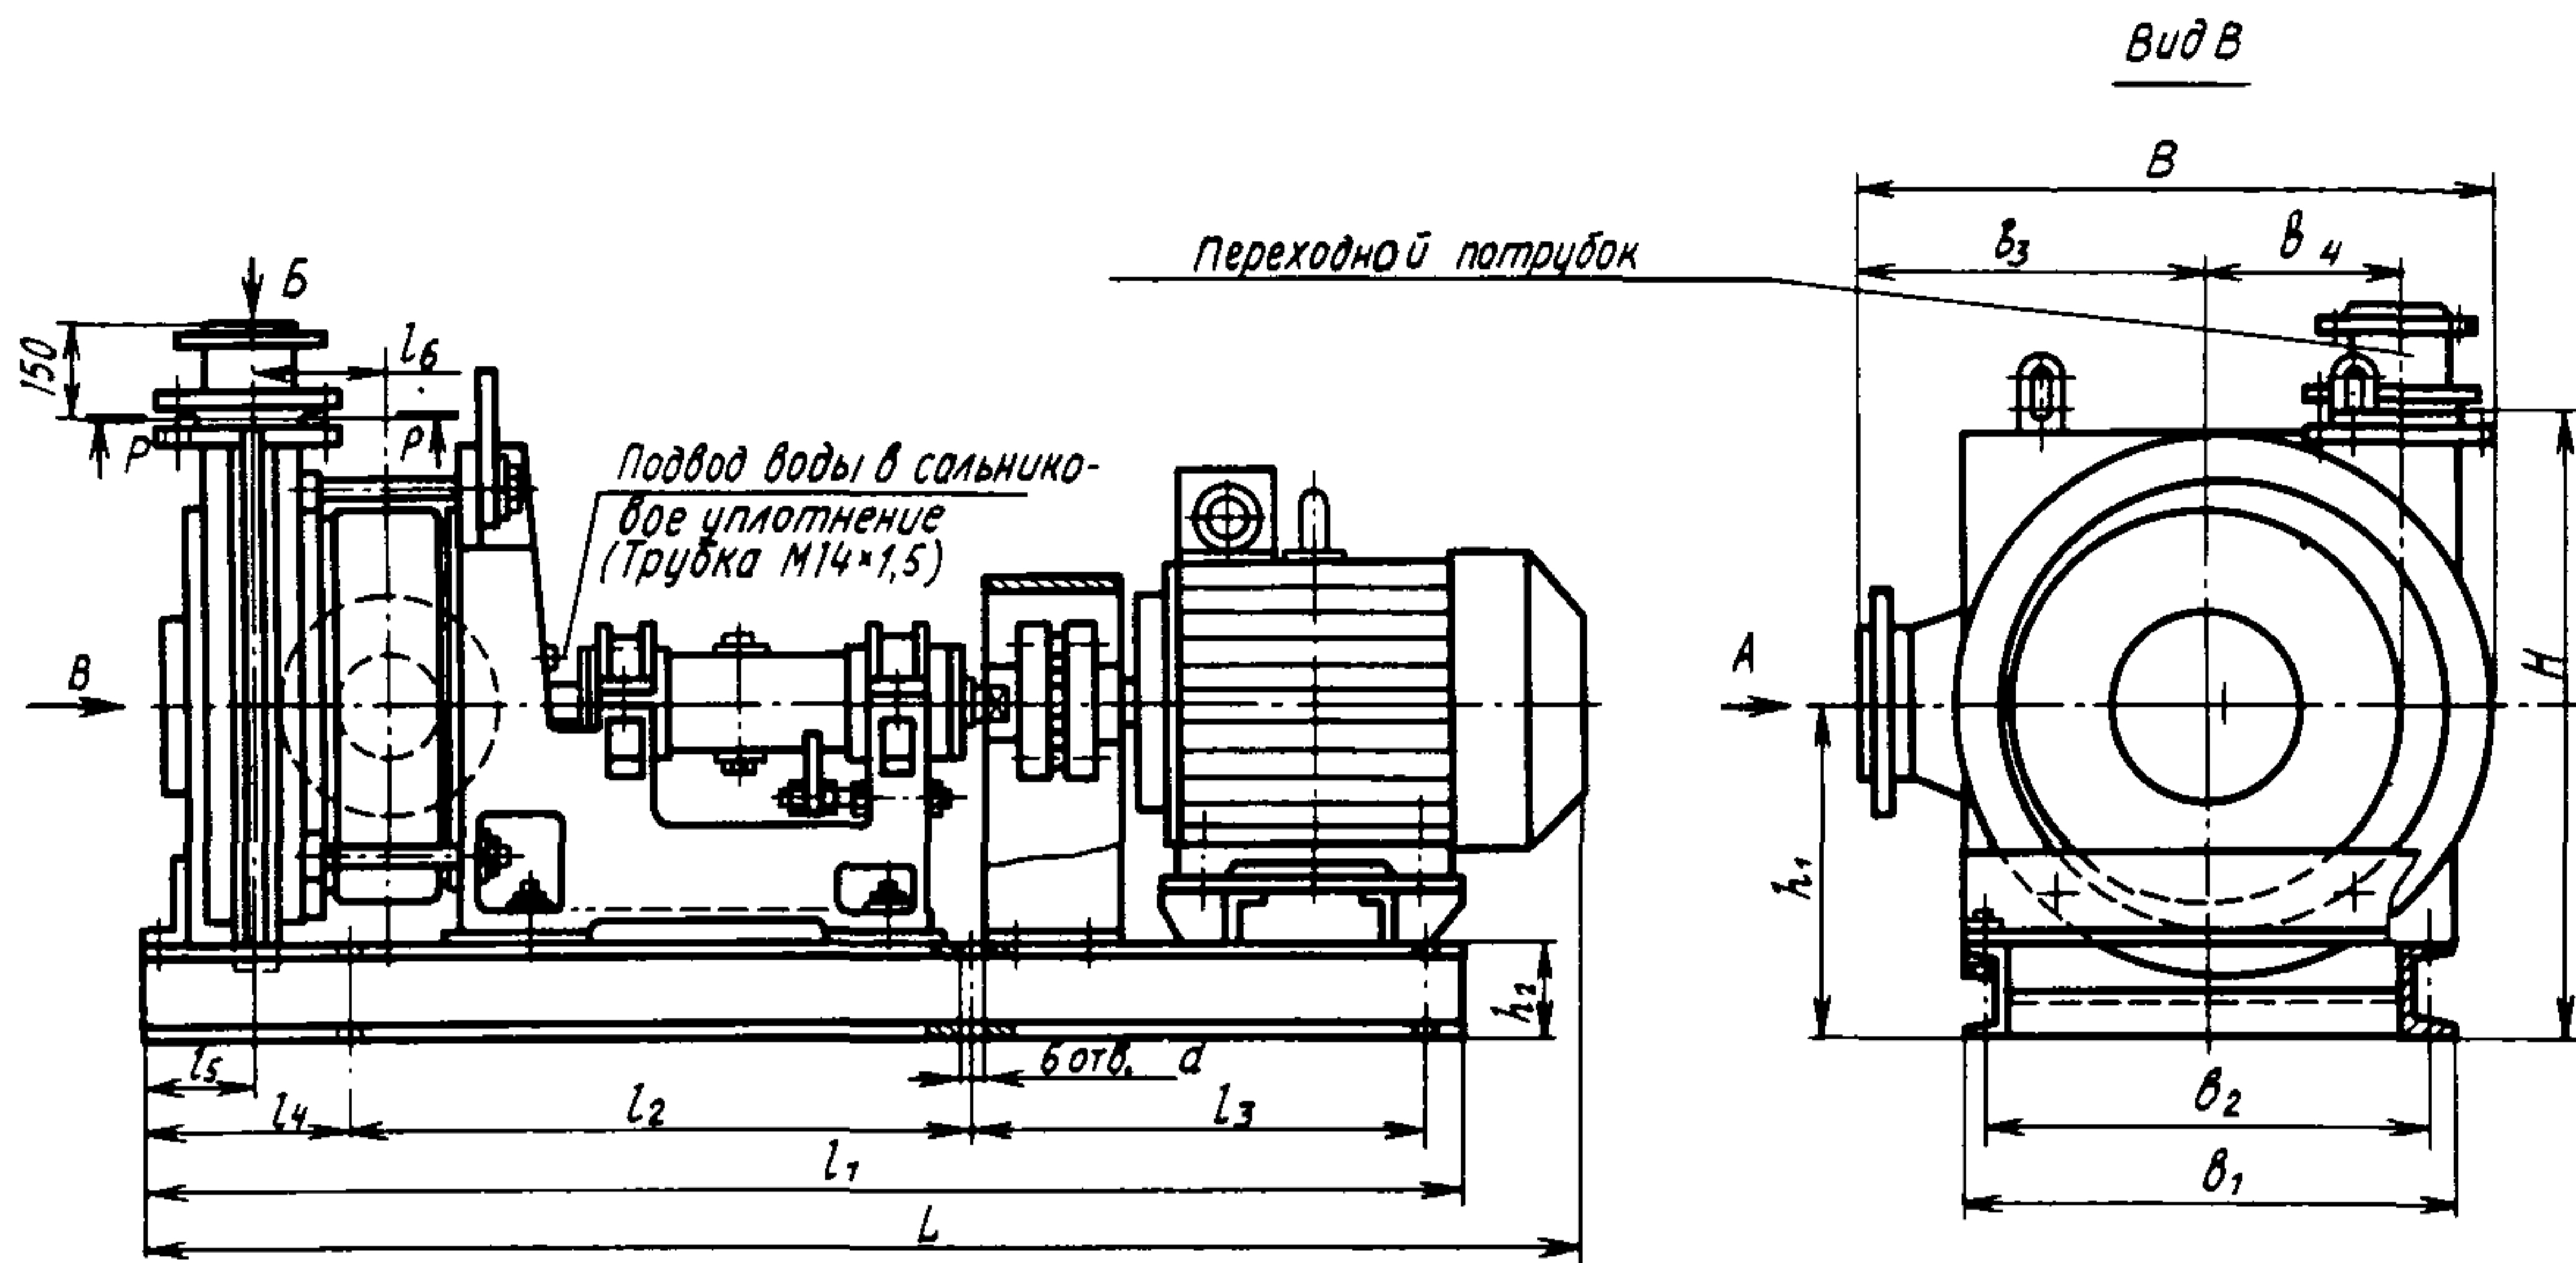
Габаритный чертеж электронасосных агрегатов типа НПБР с приводом через упругую муфту
